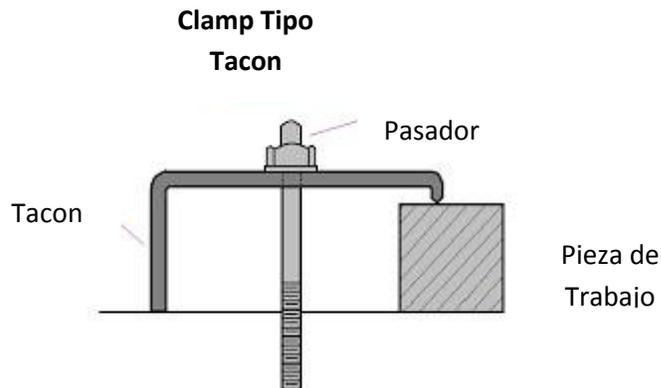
Clamp tipo tacón. Fuente: American Machinist
